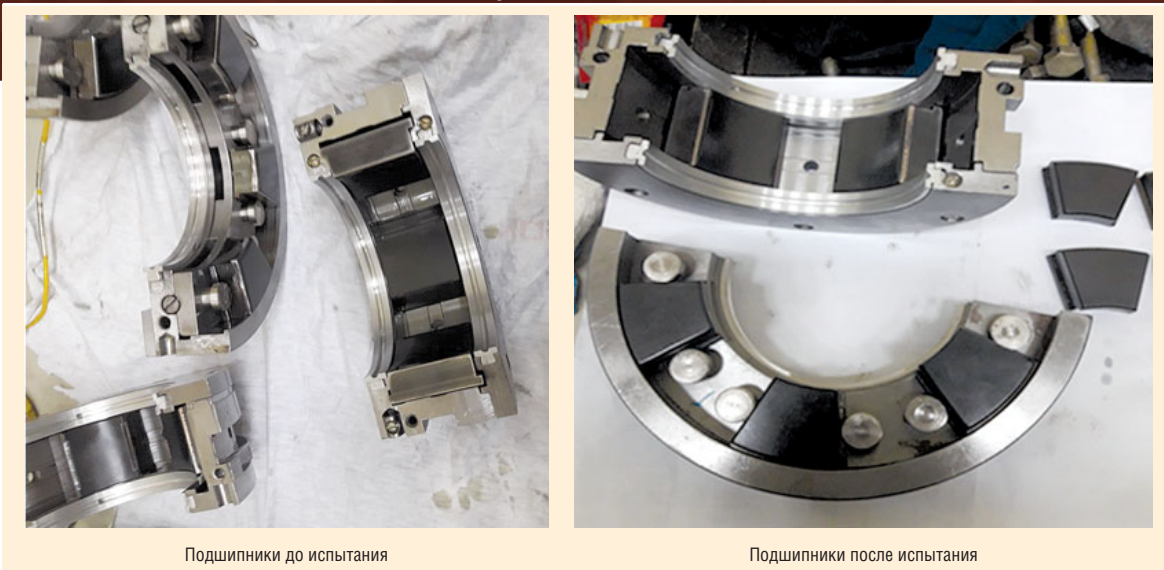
Внешний вид подшипников до и после проведения стендовых испытаний в ПНИПУ
